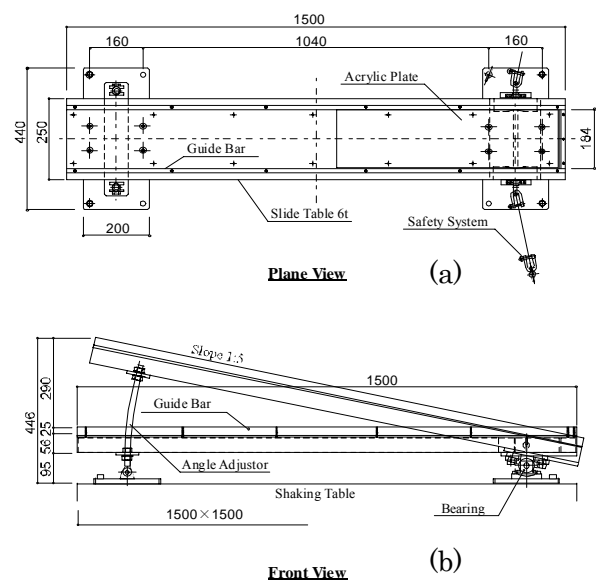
傾斜台設計図 : (a) 平面図, (b) 正面図
